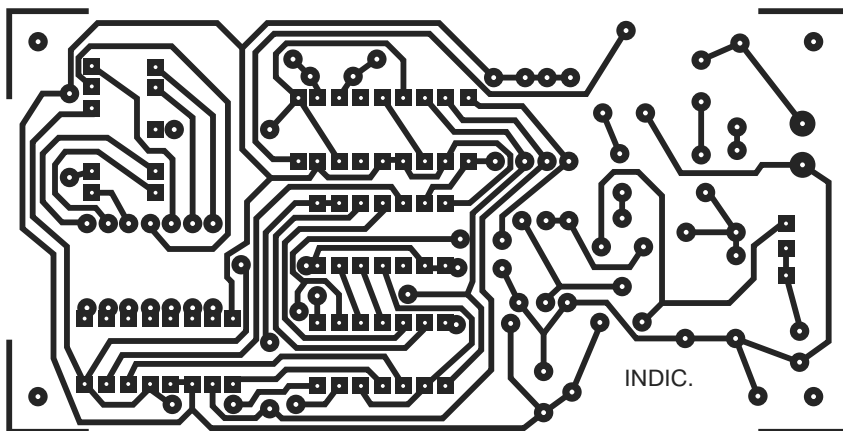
Чертеж печатной платы цифрового индикатора телефонного набора
